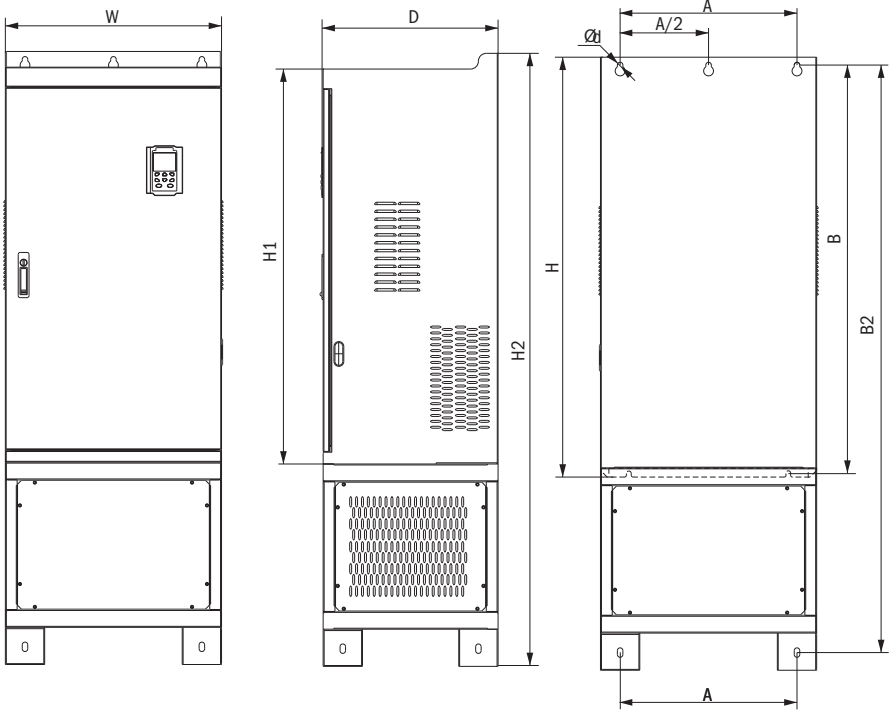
Габаритные и установочные размеры габарита 12 (280+315 кВт)
